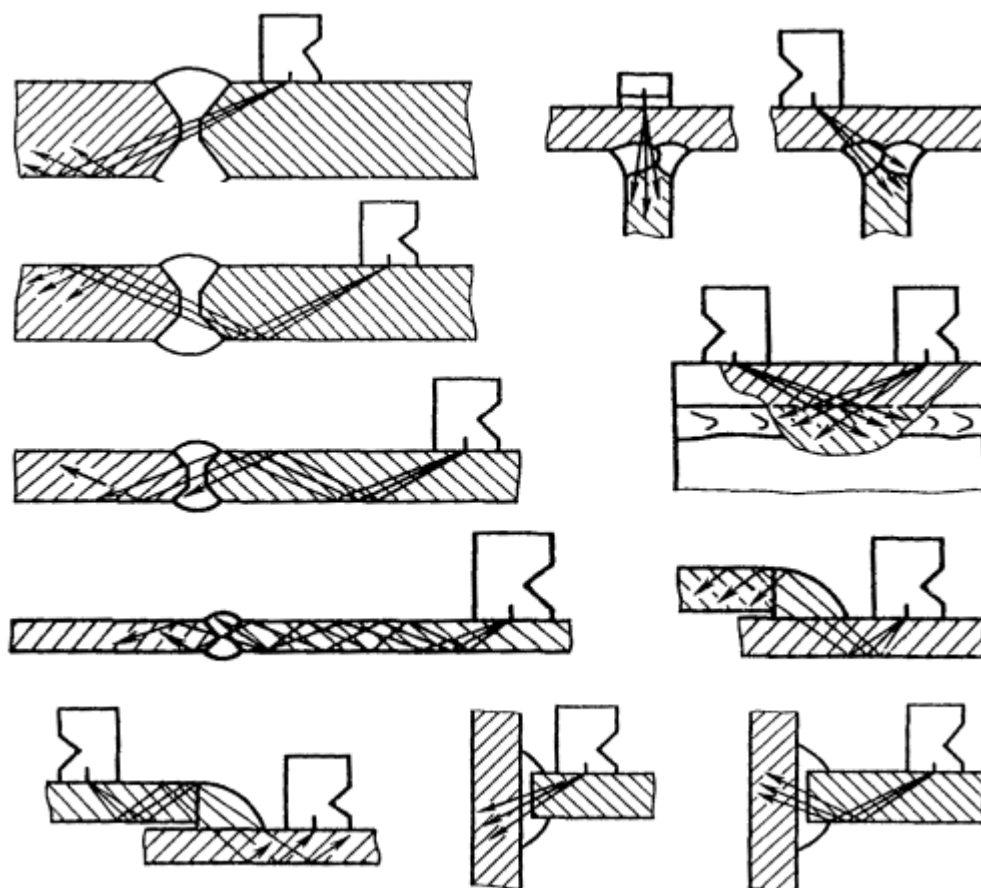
ультразвуковой контроль сварного шва
